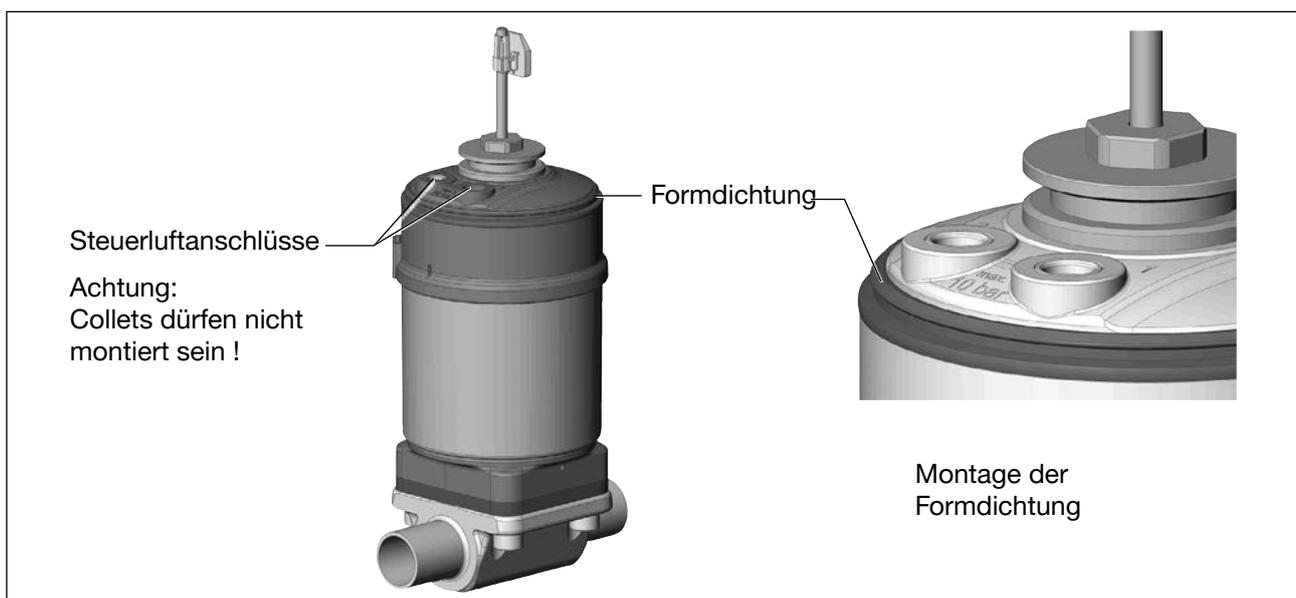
Montage der Formdichtung bei Prozessventilen des Typs 2103, 2300 und 2301
